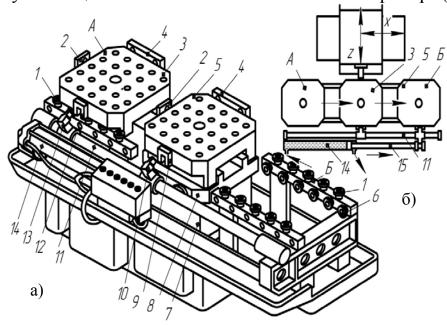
Устройство замены приспособления—спутника на станке: а — общий вид; б — схема действия
